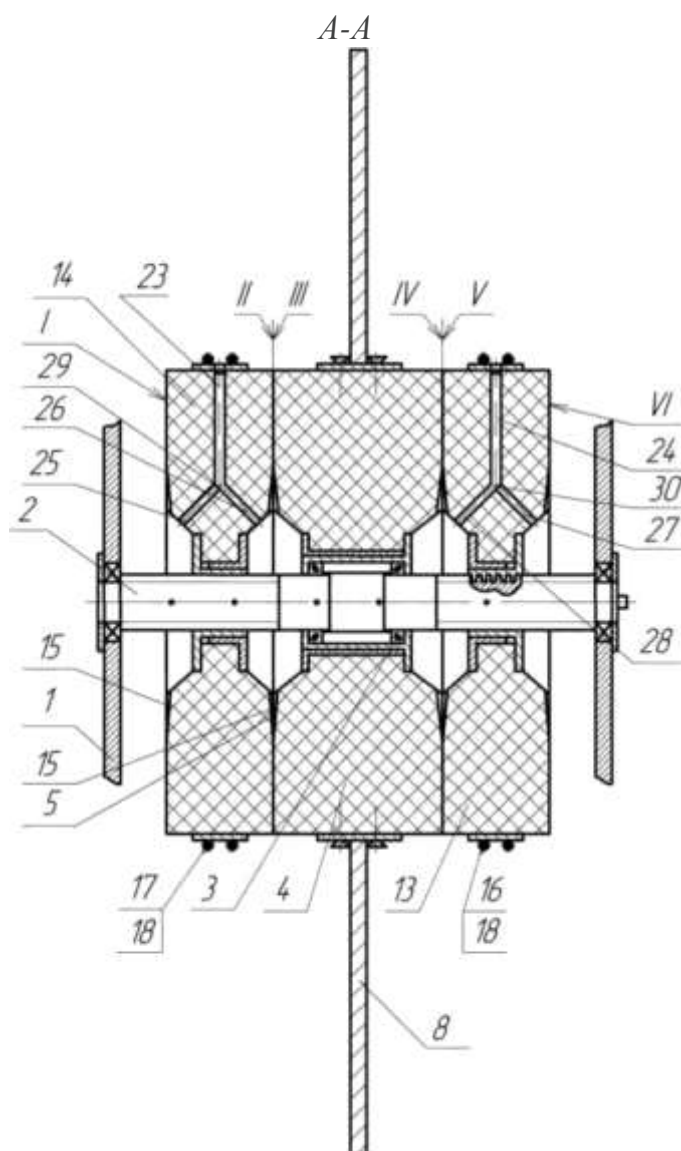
Разрез А - А конструкции применения ЛАД в жерновой мельнице с горизонтальной осью вращения для измельчения зерна: I, II, III, IV, V - поверхности жерновов с различной толщиной зазора; 2 - ось; 3 - подшипниковая опора; 4 - средний жернов; 5 - канавки среднего жернова; 8 - вторичный элемент ЛАД (алюминиевый диск); 13,14 - неподвижные жернова; 15 - канавки неподвижных жерновов,16,17 - гибкие элементы; 18 - упругий элемент; 23,24 - каналы для подачи зерна в рабочую зону; 25,26,27,28 - сообщающиеся каналы; 29,30 - затворы
